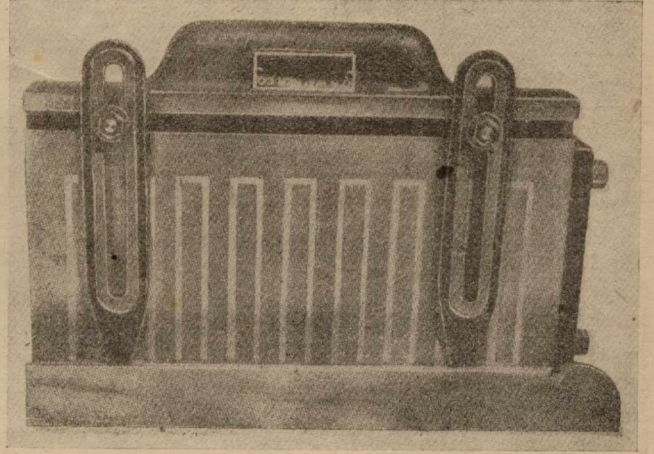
Powierzchnie robocze uchwytów magnetycznych współczesnych.
